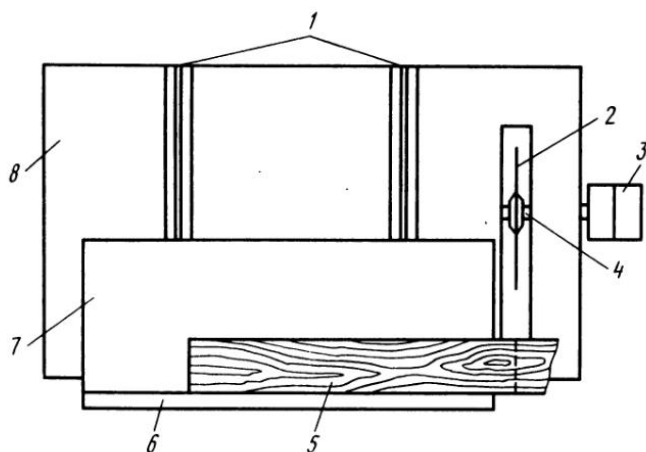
Поперечный раскрой досок на универсальном круглопильном станке с помощью каретки:
